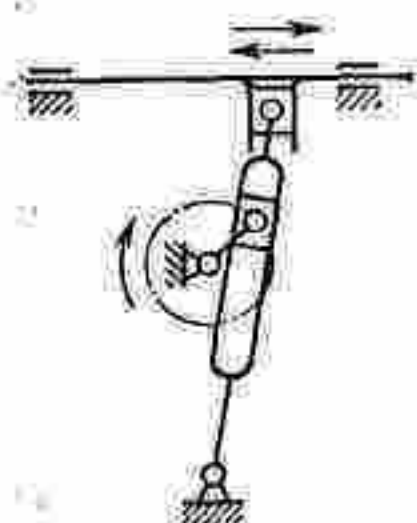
Многозвенный плоский кривошипно-кулисный механизм привода главного движения поперечно-строгального станка.
